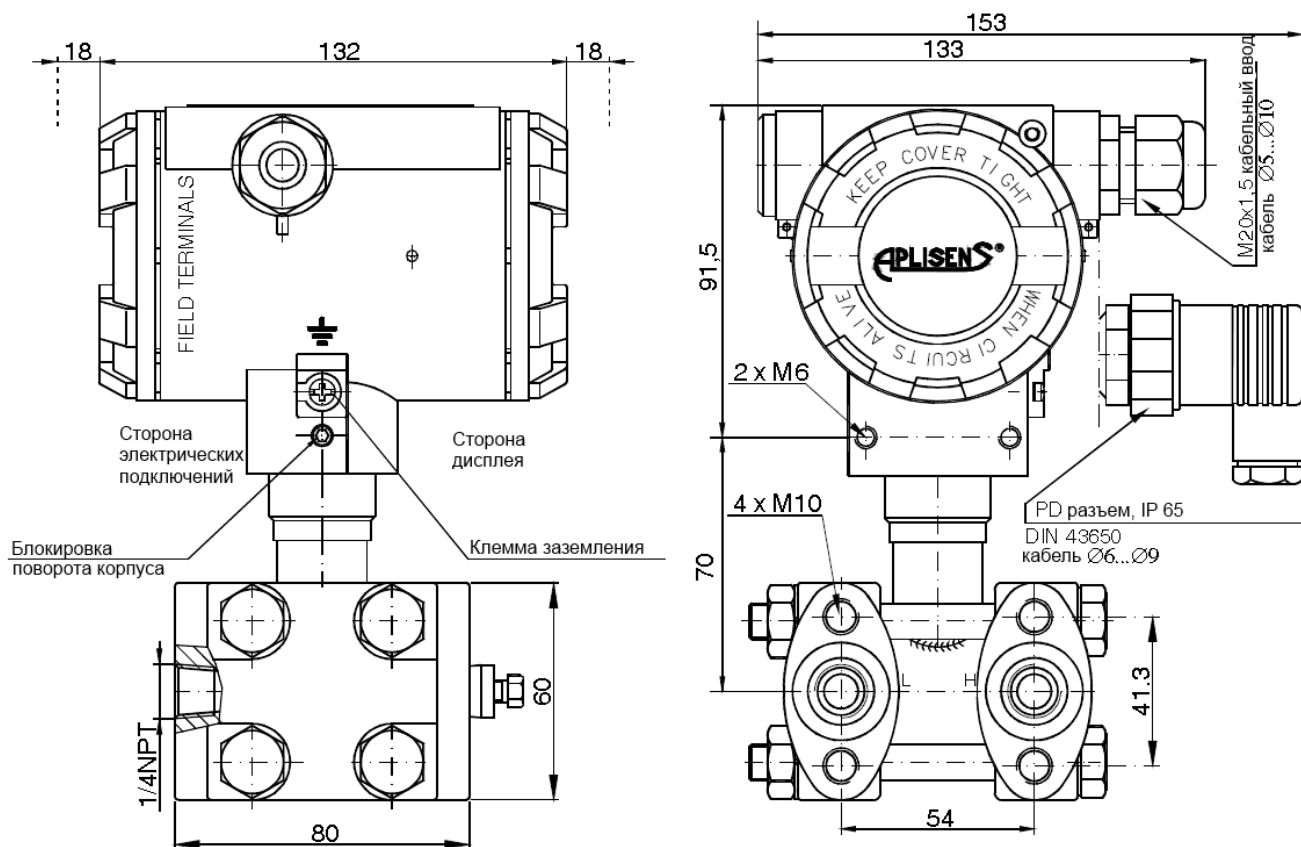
Внешний вид, установочные и присоединительные размеры преобразователей APR-2000.Safety/ALW с присоединением С
